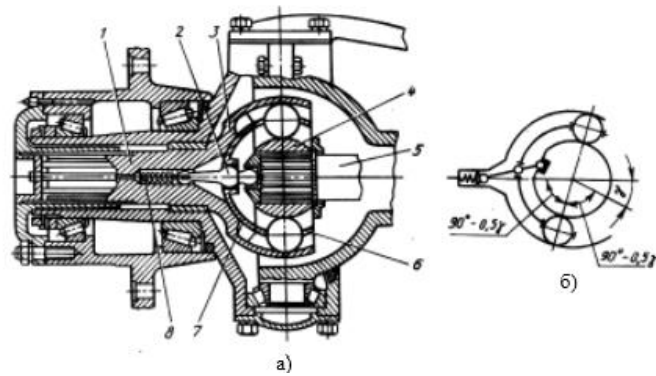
Шариковый карданный шарнир с делительным рычажком (типа “Рцепп”): а – установка шарнира в приводе переднего колеса; б – схема шарнира: 1 и 5 – валы; 2 – делительный рычажок; 3 – чашка; 4 – сферический кулак; 6 – сепаратор; 7 – направляющая чашка; 8 – пружина
